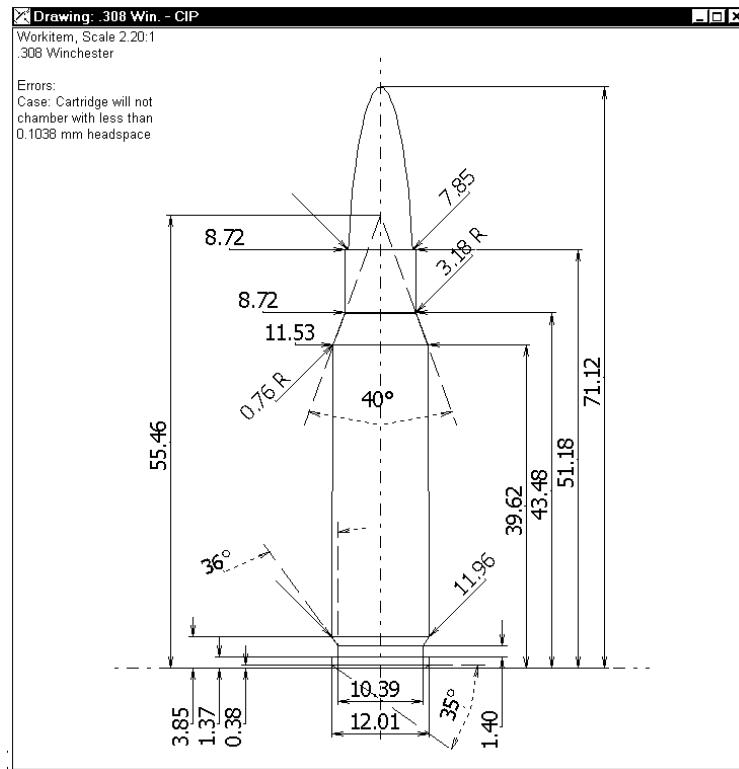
Patrone, Umrisszeichnung mit Bemaßung
